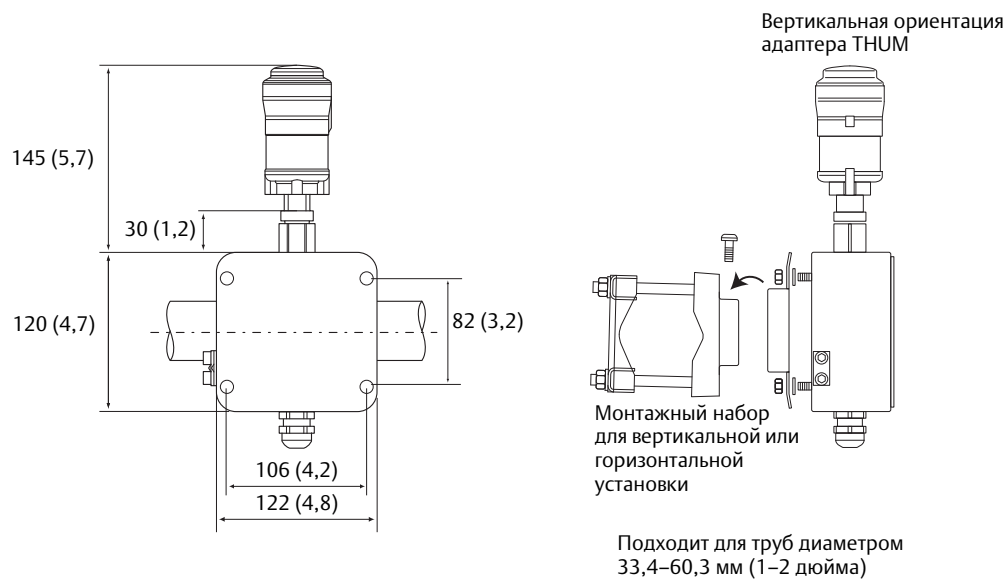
Размеры распределительного узла резервуара Rosemount 2410
